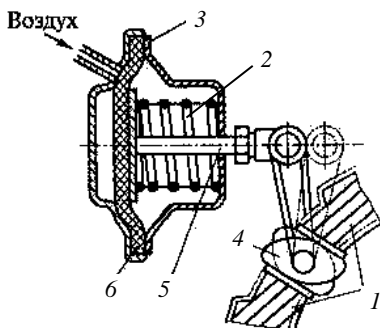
Пневматический привод тормозного механизма:
